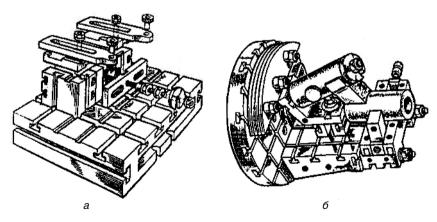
Приспособление для механической обработки: а — для обработки отверстий; б — для токарных работ
